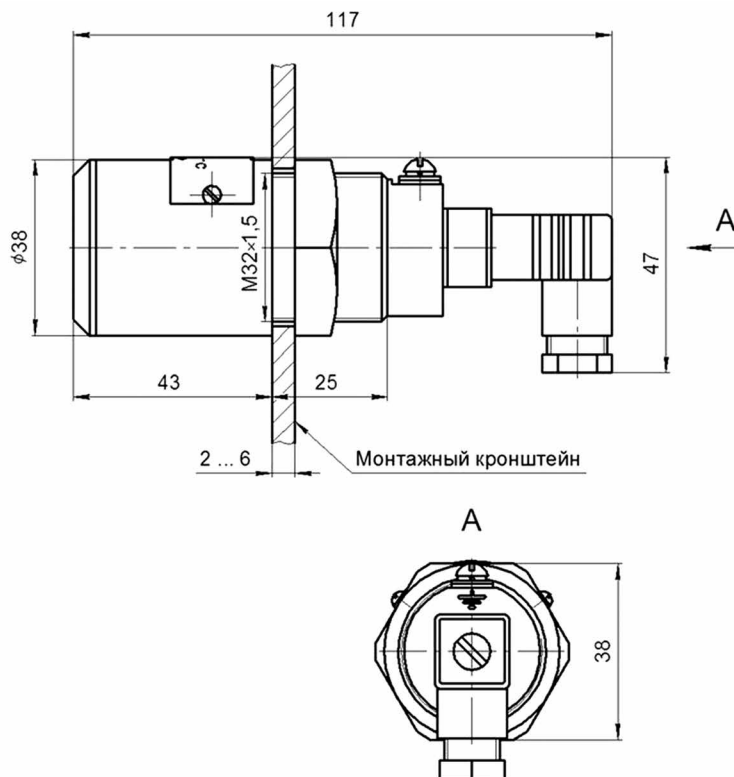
Габаритные и присоединительные размеры ИЗВ-301-И
